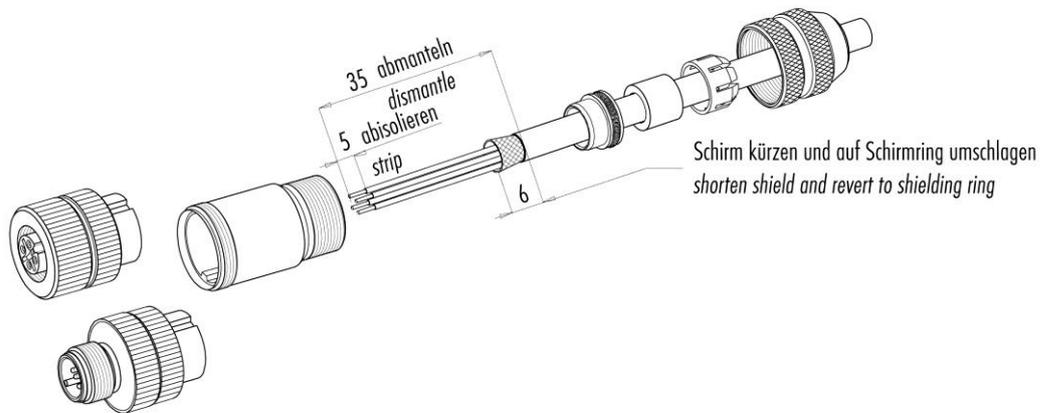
Montageanleitung für geschirmte Steckverbinder Anschlüsse 1, 2, 4 und 5
